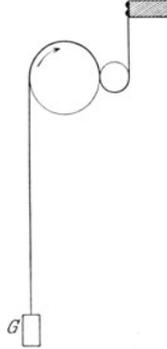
Schema eines Riemenfallhammers mit befestigtem Riemenende.
